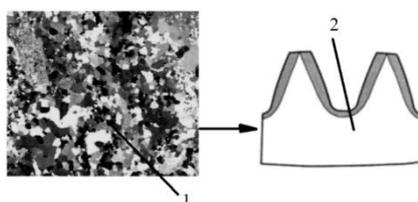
Цементация зубчатого колеса, карбидная фаза и упрочнение зубчатого колеса
